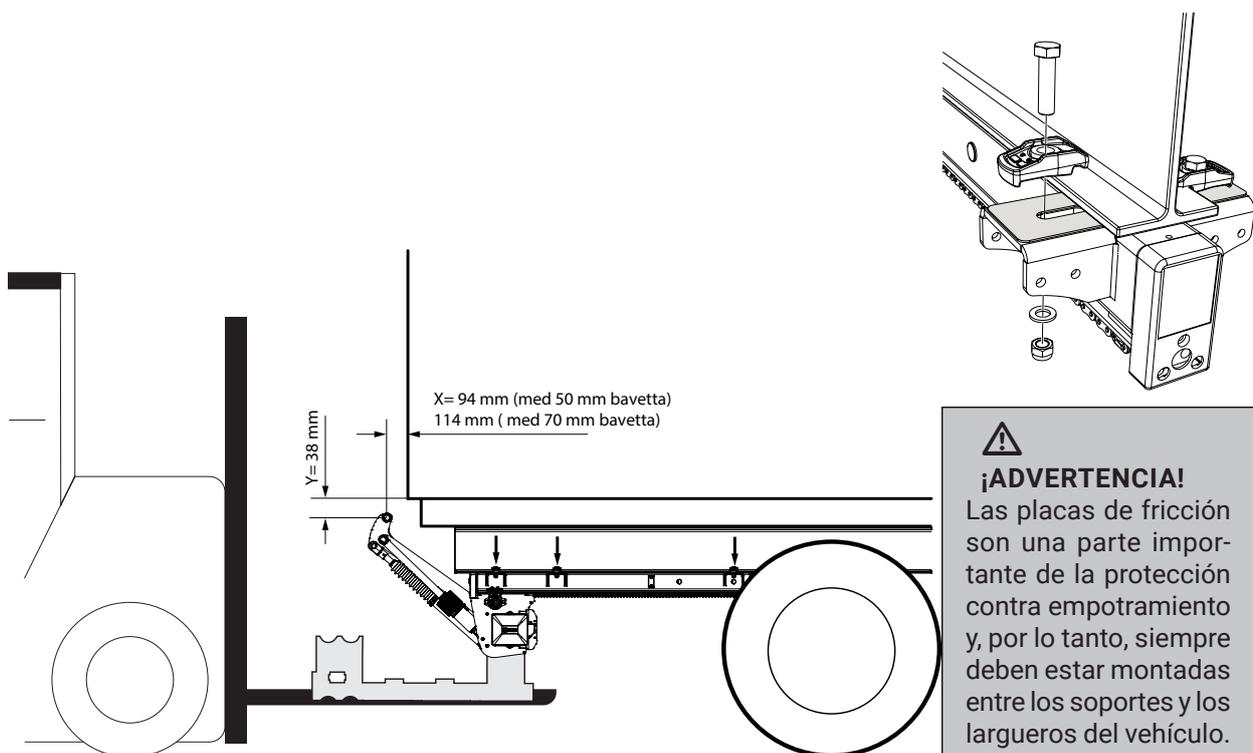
Montaje de la estructura del elevador en la posición de trabajo
